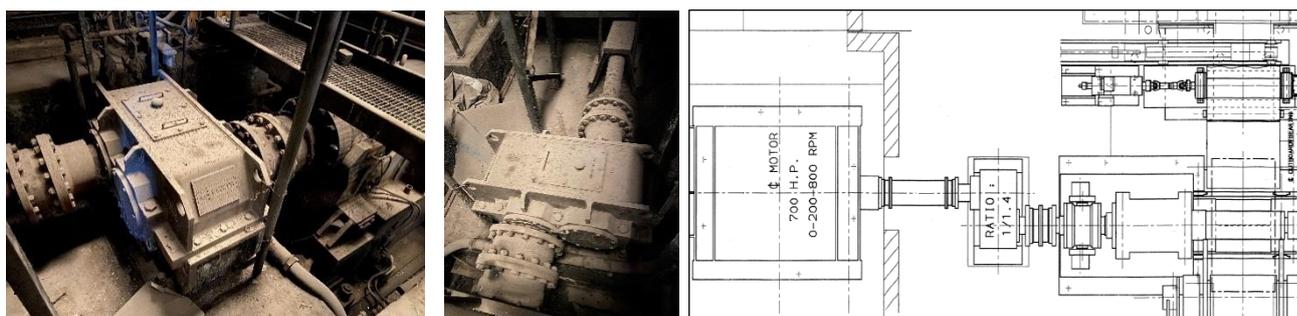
Acoplamiento, eje de transmisión y reductor de mandril enrollador.
